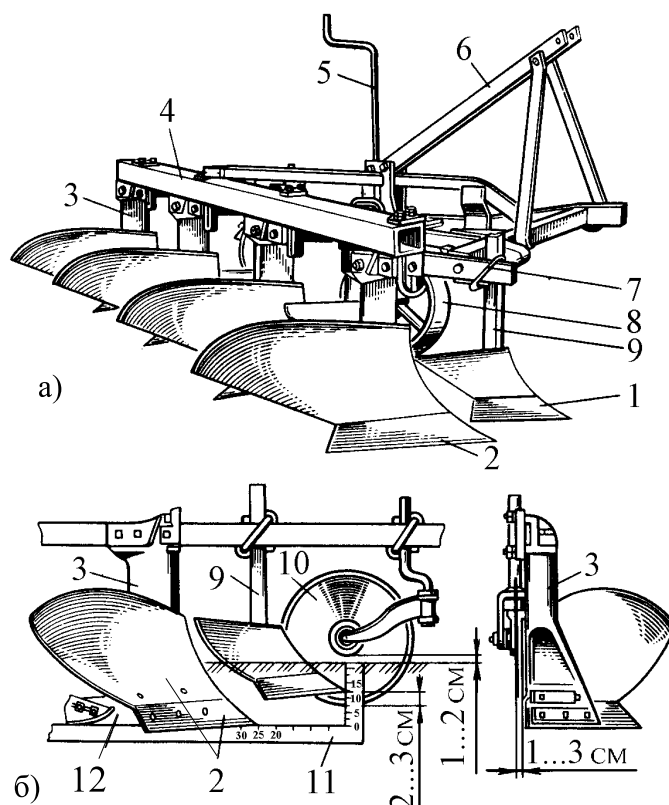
Плуг лемешный навесной ПЛН-4-35: а – схема плуга; б – установка предплужника и дискового ножа; 1 – предплужник; 2 – лемех основного корпуса плуга; 3 – стойка корпуса; 4 – рама; 5 – винт; 6 – навесное устройство; 7 – стремянка; 8 – опорное колесо; 9 – стойка предплужника; 10 – дисковый нож; 11 – установочный угольник-линейка; 12 – полевая доска
